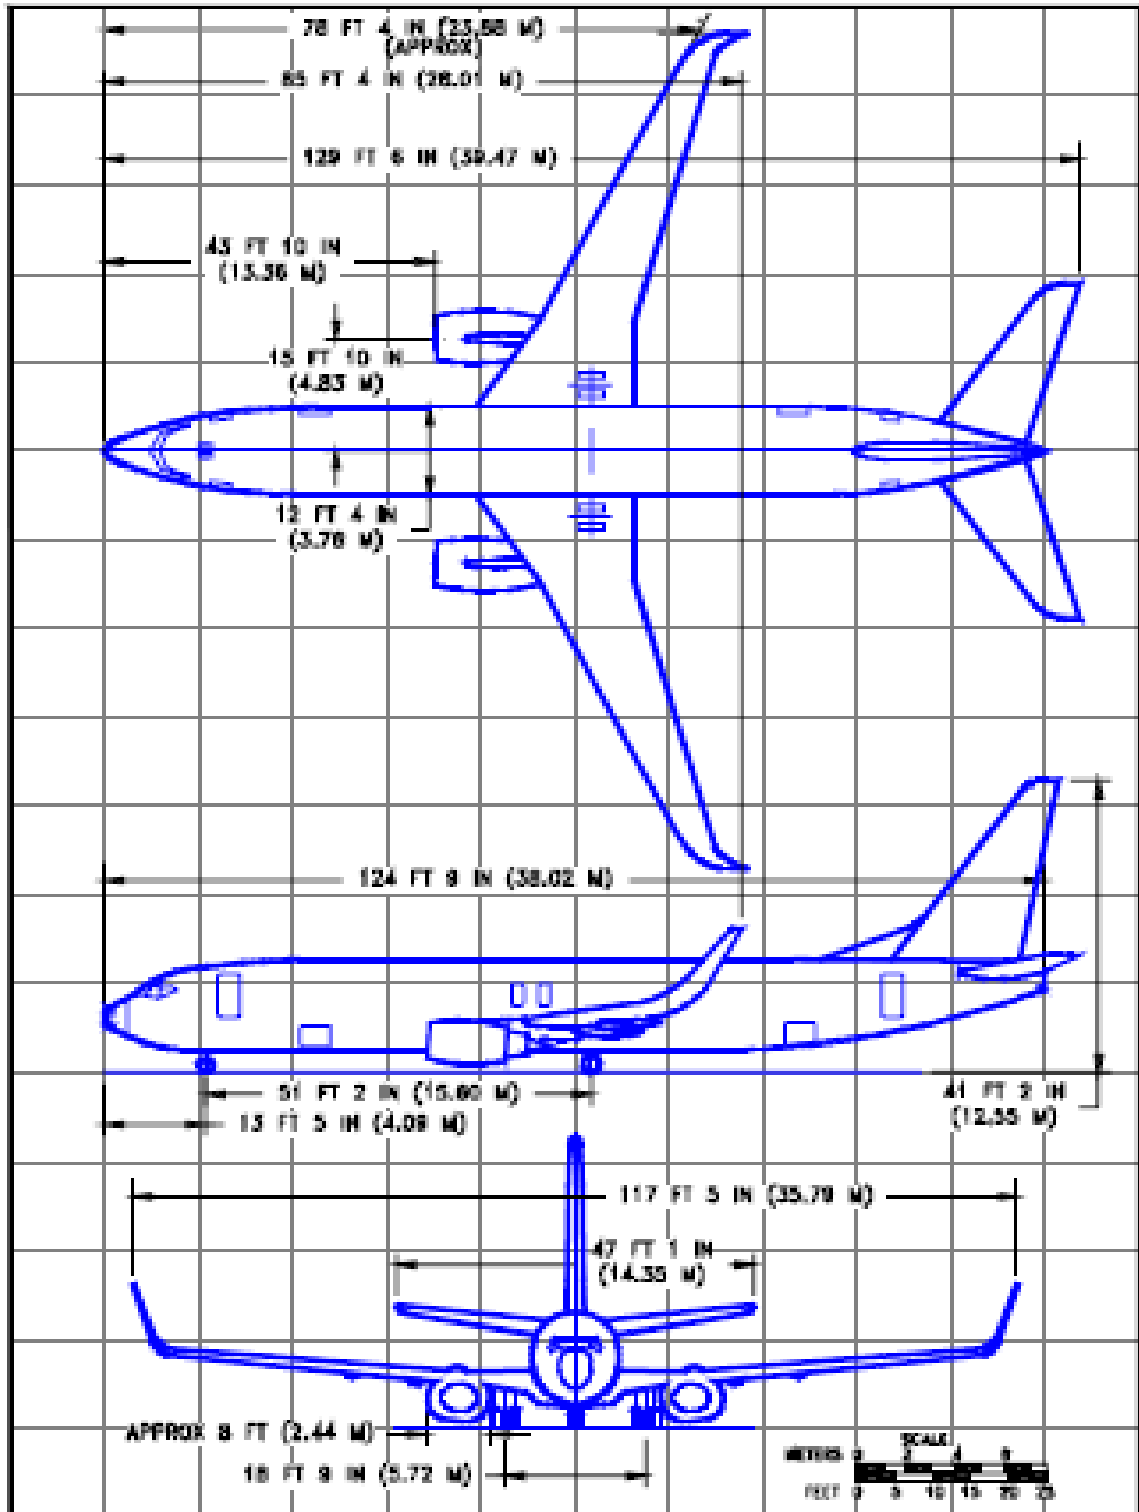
Arrangement générale et les principales dimensions du B737-800 avec des winglets
